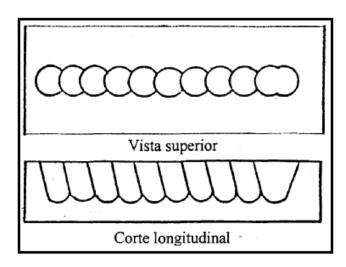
Soldadura obtenida por el proceso TIG con arco pulsado
